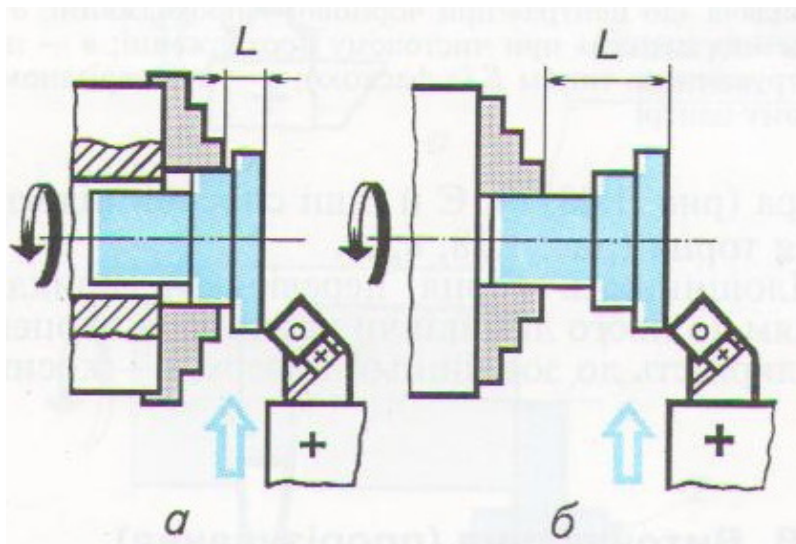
Виліт заготовки з патрона при підрізуванні торця:
